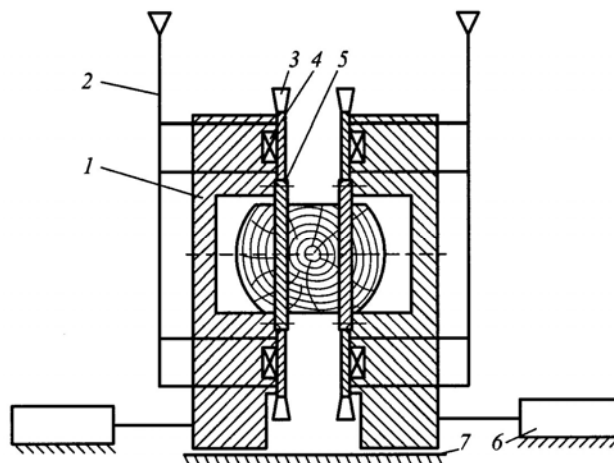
Конструкция сдвоенного станка с кольцевыми пилами
